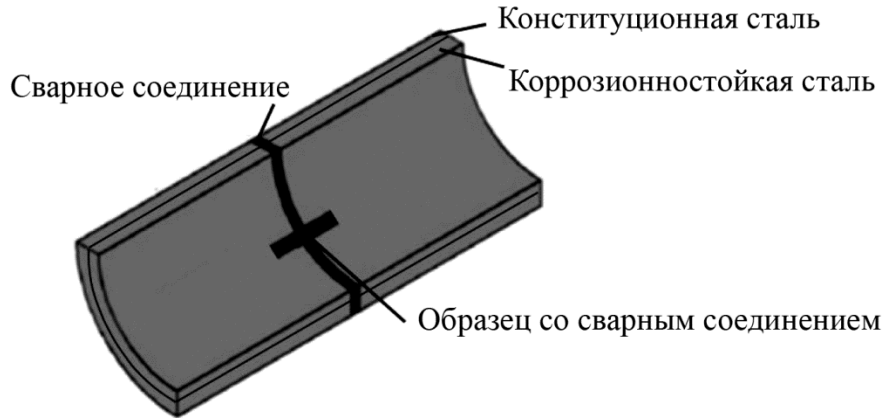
Схема вырезки образцов со сварным соединением
